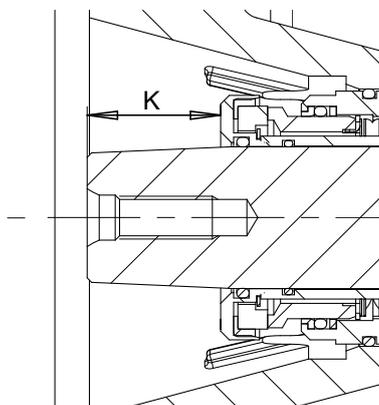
Medida de control "K" desde el extremo del eje hasta el cierre mecánico
